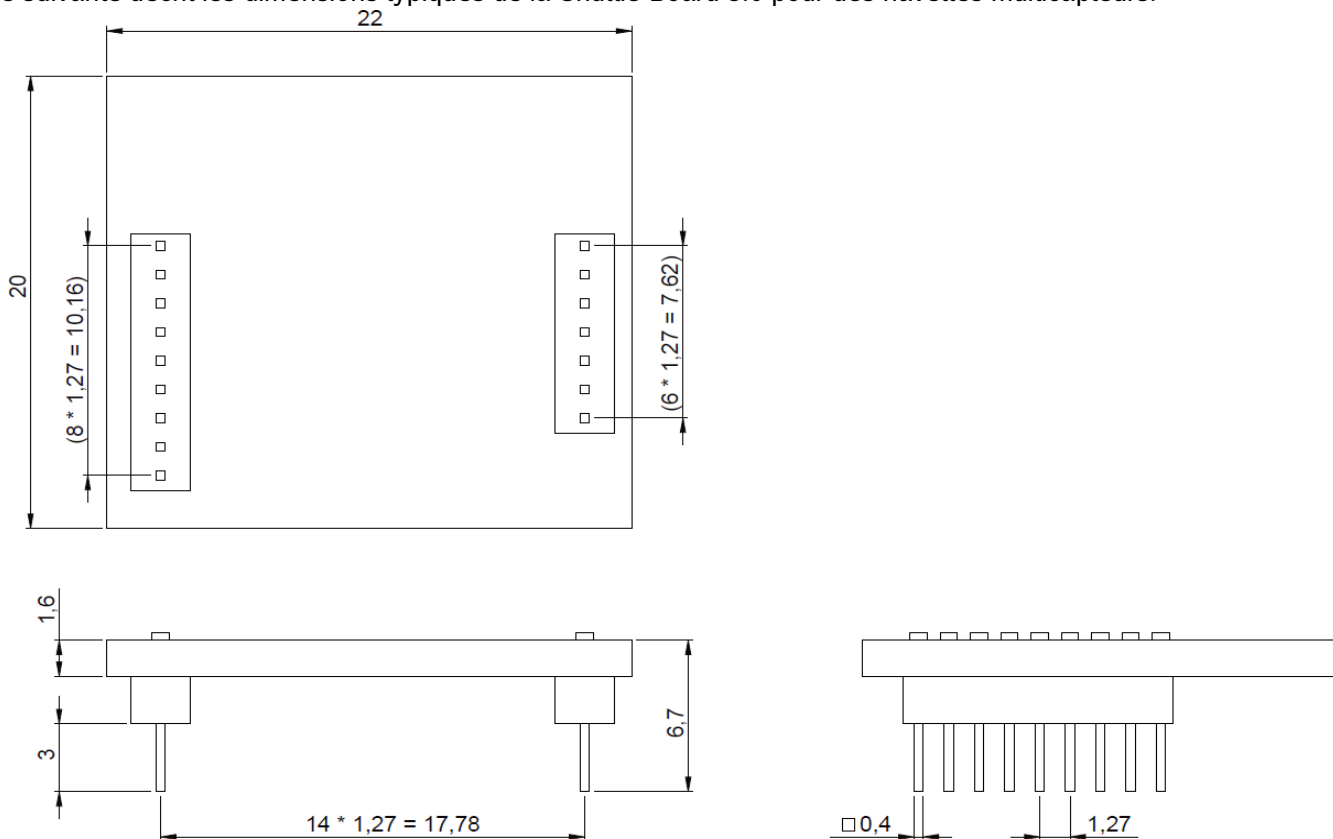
Dimensions de la carte Shuttle Board 3.0 multiresistor
